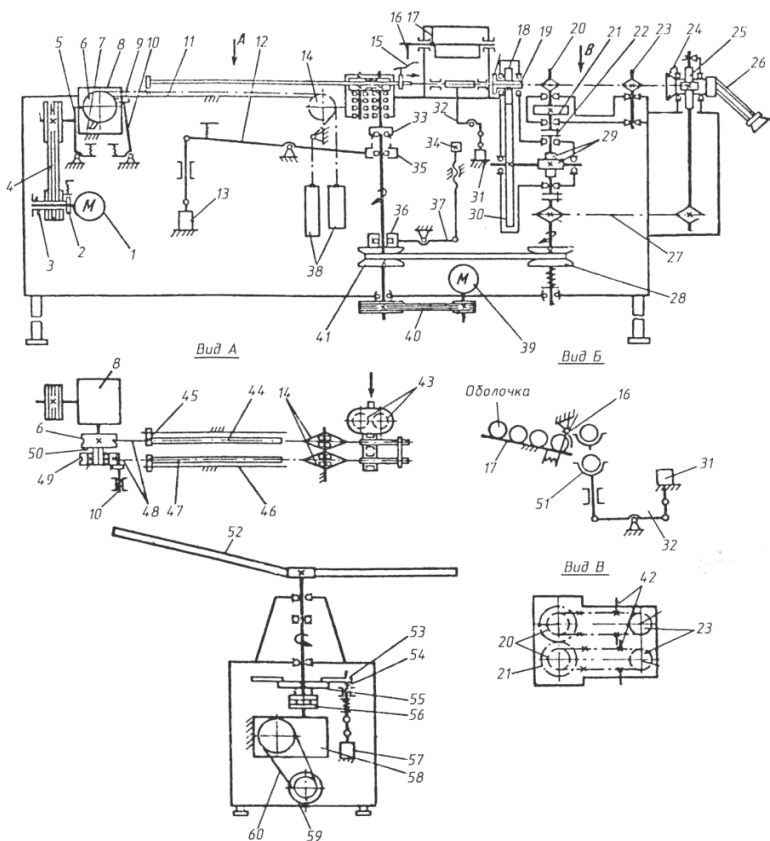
Кинематическая схема агрегата В6-ФСБ:
